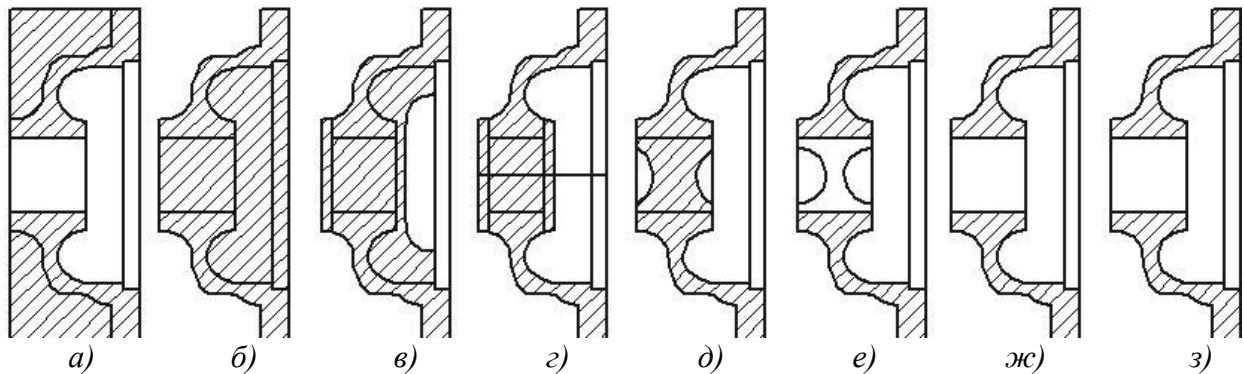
Види заготовок для виготовлення деталі типу «Кришка корпусу»
